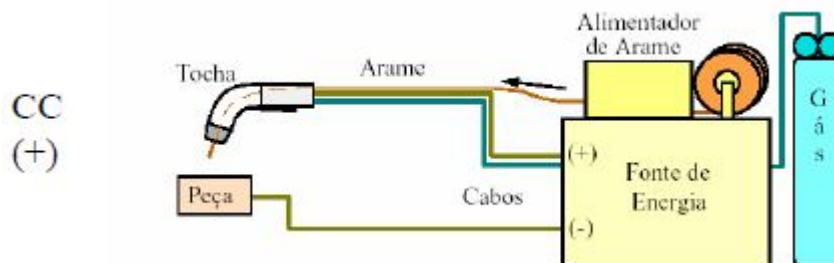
Equipamento básico para soldadura MIG/MAG.
